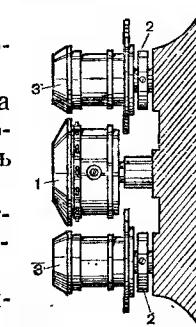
Взаимное расположение барабана и роликов: 1 — барабан; 2 — установочные кольца; 3 — ролики
